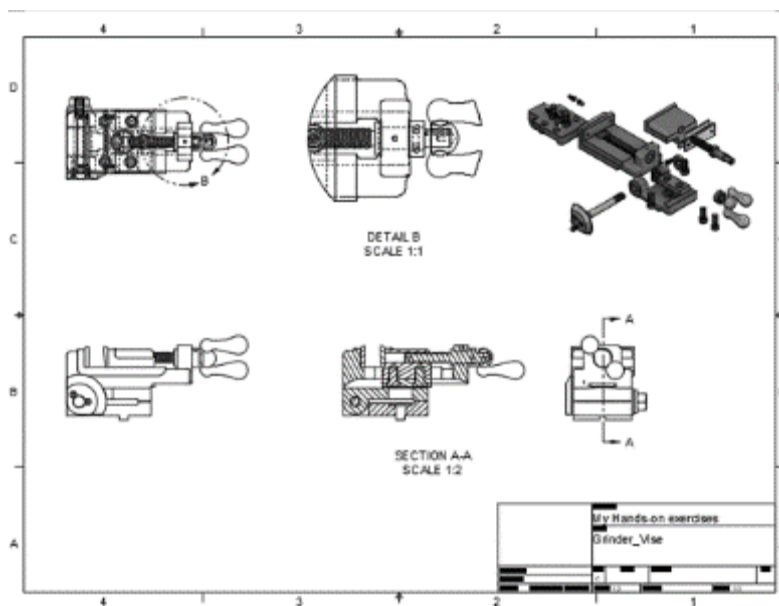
Desenho Técnico base realizado em Autodesk Fusion360®, com vistas, pormenor, secção e axonometria explodida (Autodesk, n.d.).
